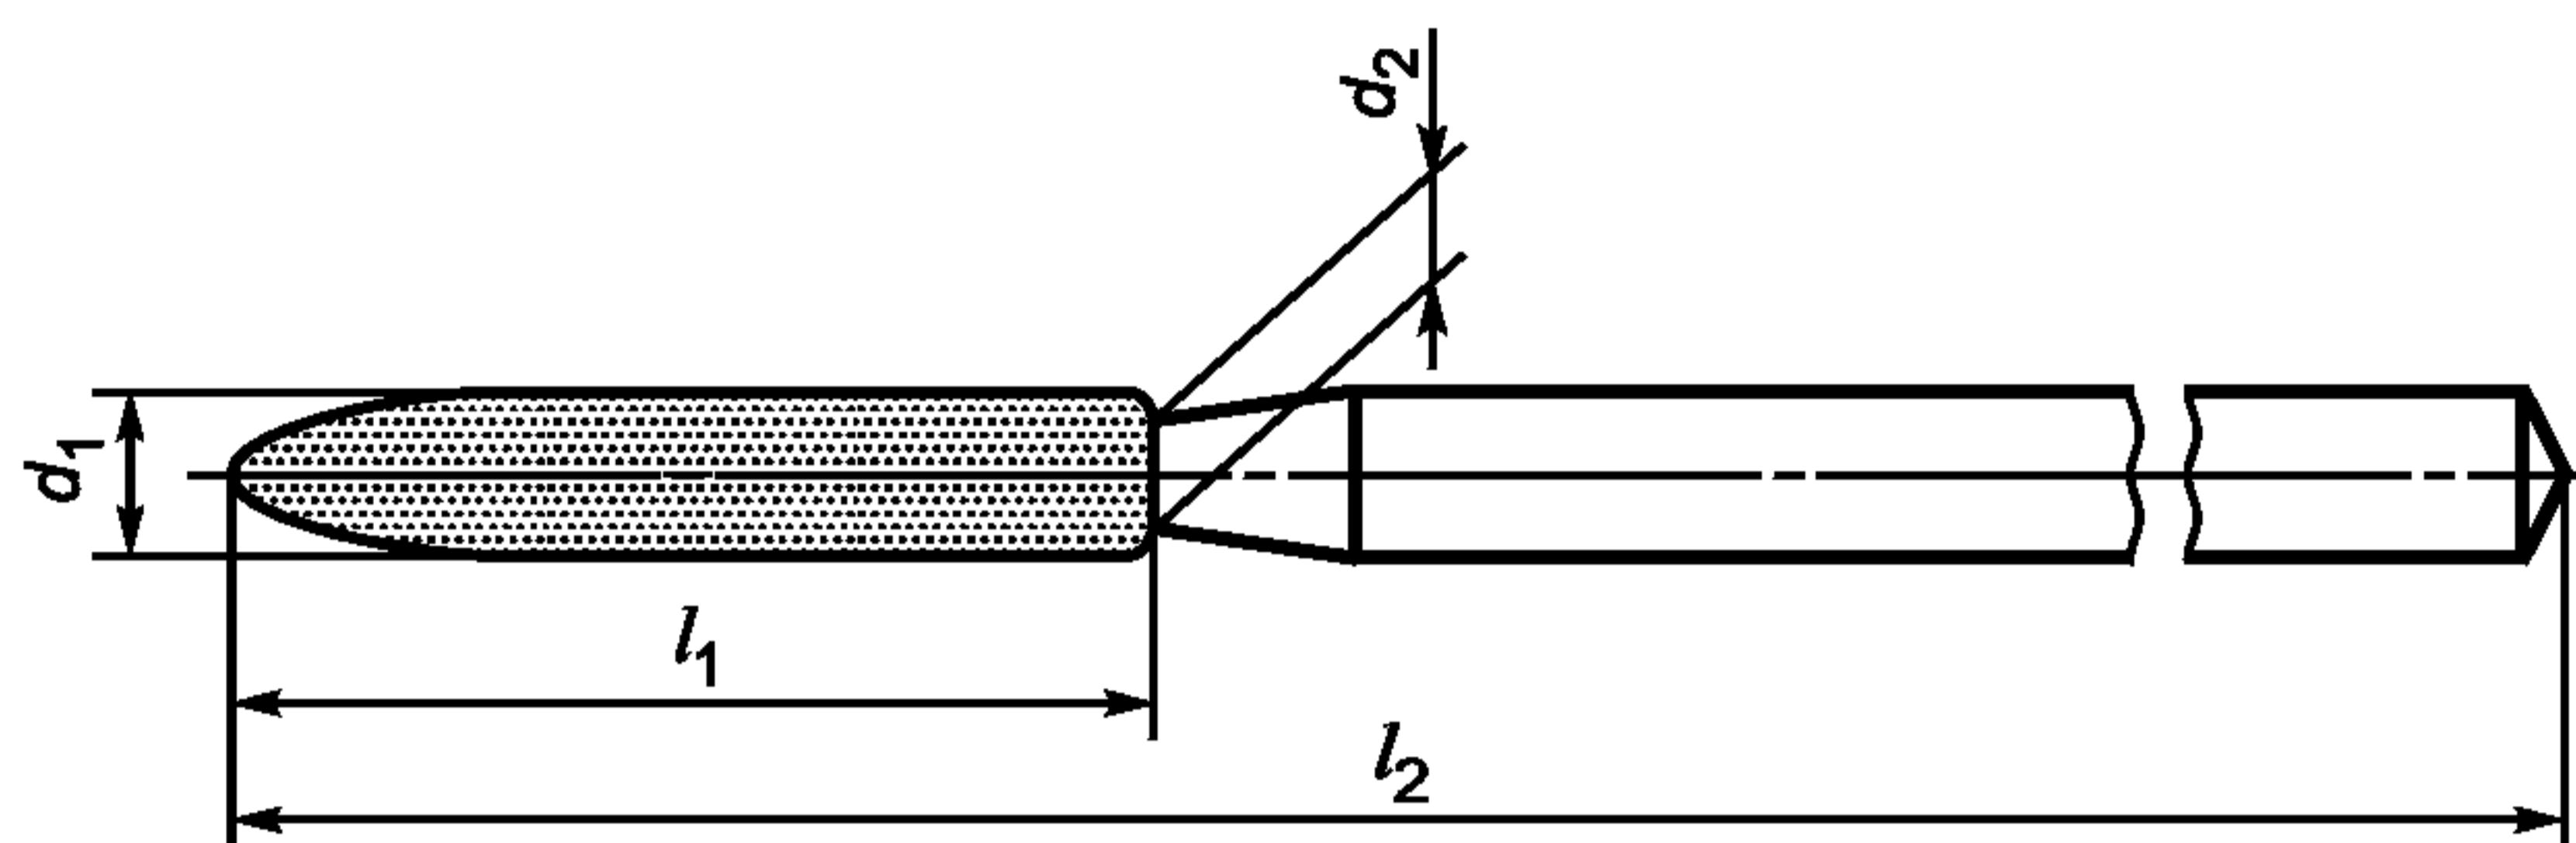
Цилиндрическая с огибалым концом рабочая часть с длиной головки 10,0 мм
